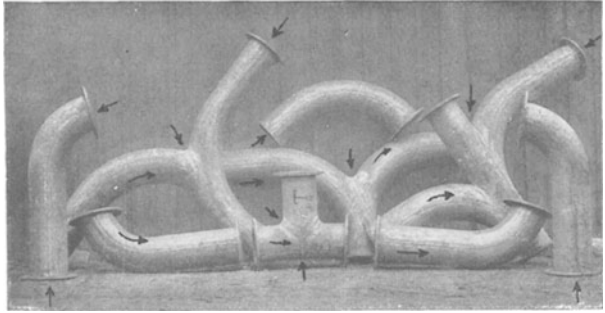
Gruppe geschweißter Kupferrohr-Formstücke.
